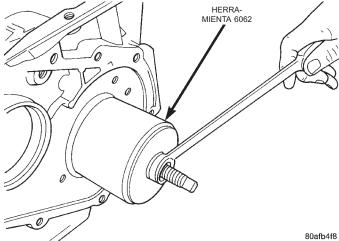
Desmontaje de la cubeta externa del cojinete transmisor
